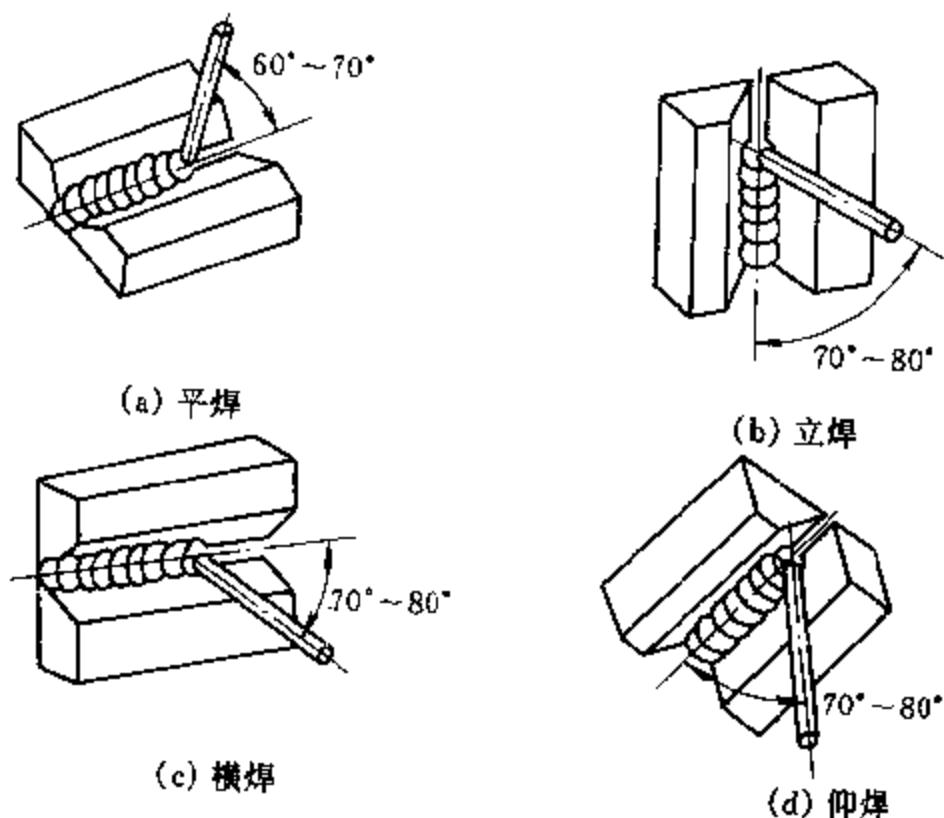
各种位置灭弧焊时焊条倾角
